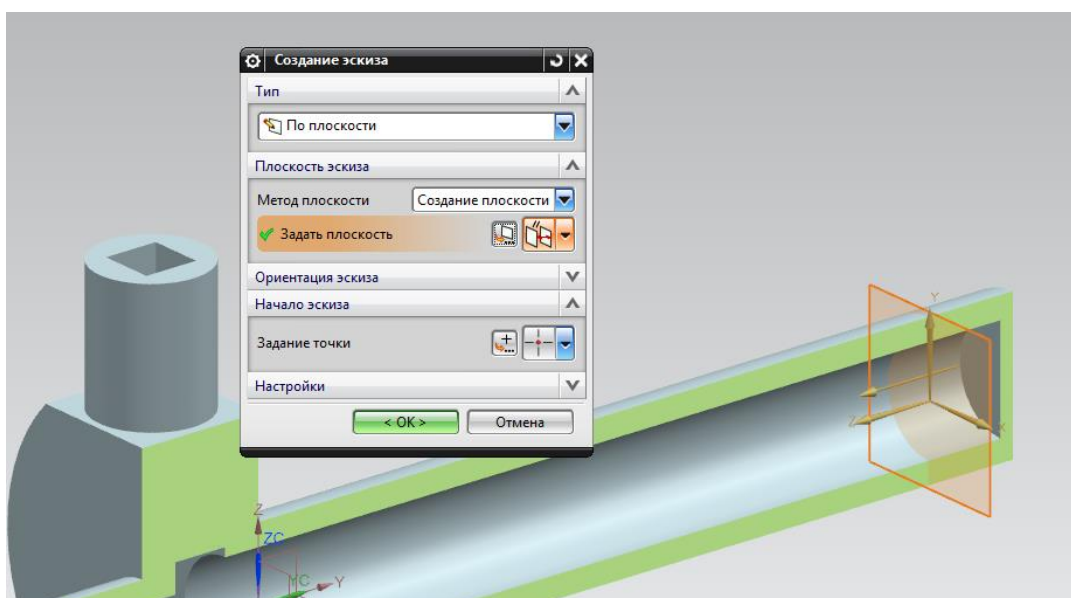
Расположение плоскости эскиза развихрителя
